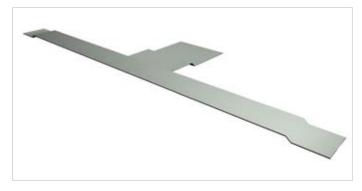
Chapa cubrecables plegada, vista desde arriba
